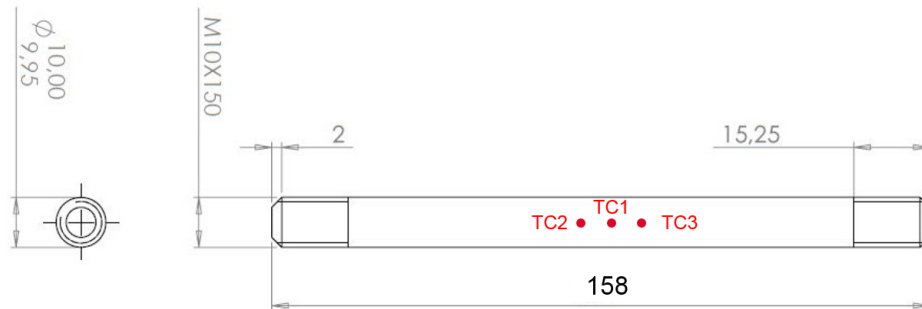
Éprouvette Gleeble en acier 316L(N). Dimensions en mm
